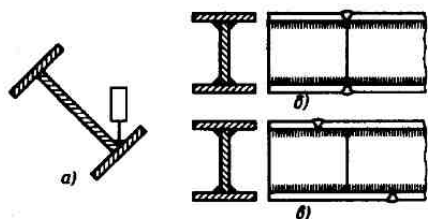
Выполнение швов двутавровой балки (а) и типы стыков сварных блоков (б, в)
